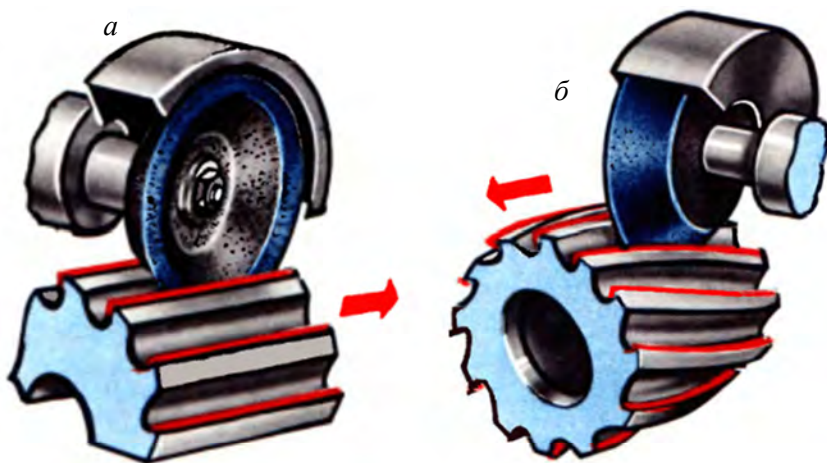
Схема заточки фрезы по передней поверхности:
